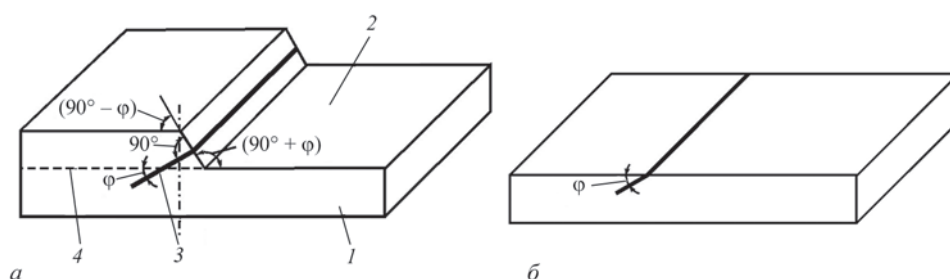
Схема реалізації способу виготовлення (а) СЗ для імітації нахилених тріщин (б): 1 – заготовка; 2 – клиноподібний виріз; 3 – дефект; 4 – лінія видалення вирізу
